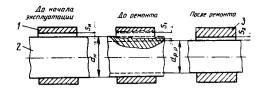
Схема восстановления зазора в сопряжении шейка вала — подшипник скольжения способом ремонтных размеров:
